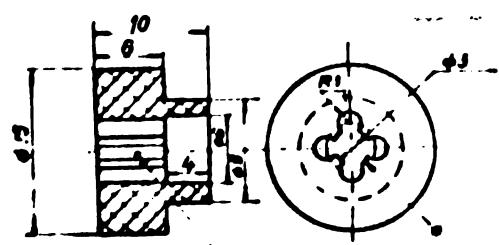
Piesă duză din ceramică prelucrabilă prin ultrasunete.
